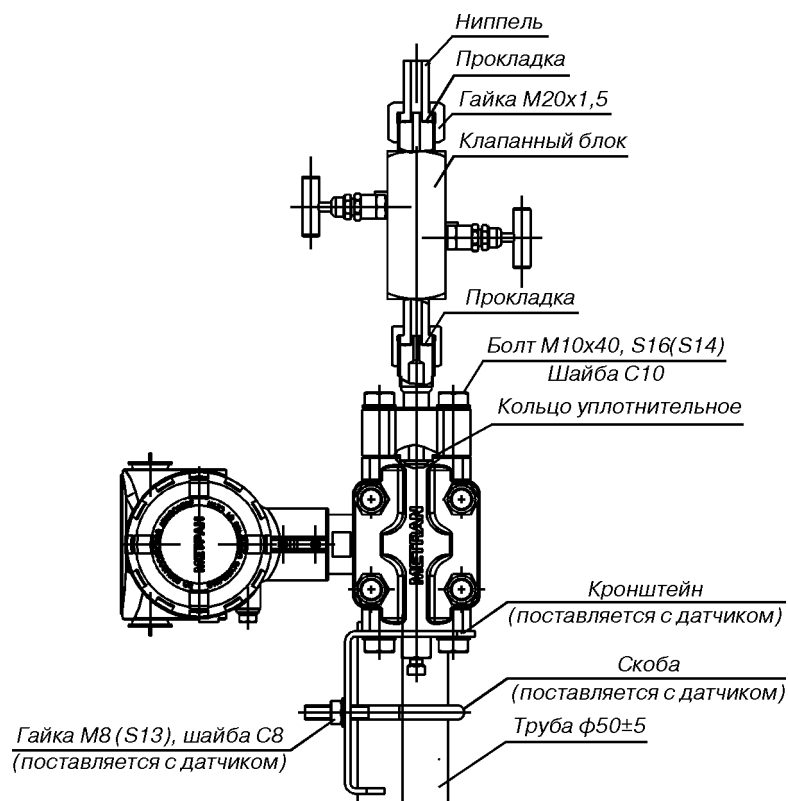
Пример монтажа датчика давления Метран-150CG с установленным клапанным блоком 0106 М Т 2 и кронштейном для датчика давления. Габаритные и присоединительные размеры см.рис.21.
